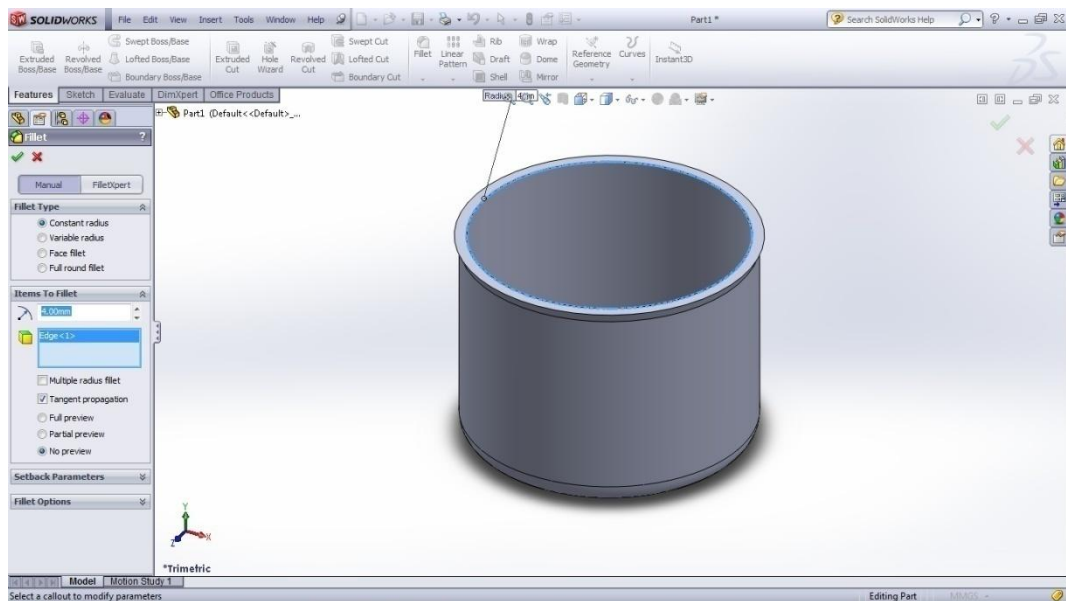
Sketsa 3D *Extruded cut* pada *inner cooking pan
